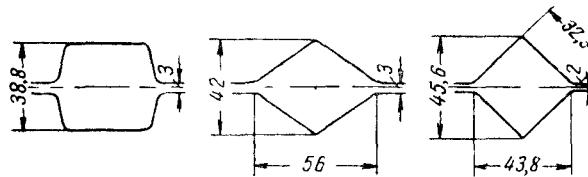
Калибровка квадратной стали 32 × 32 мм
